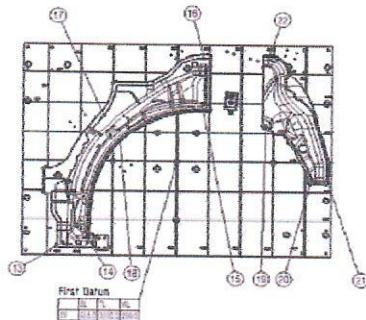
Pengukuran untuk Datum Plan No. 7
